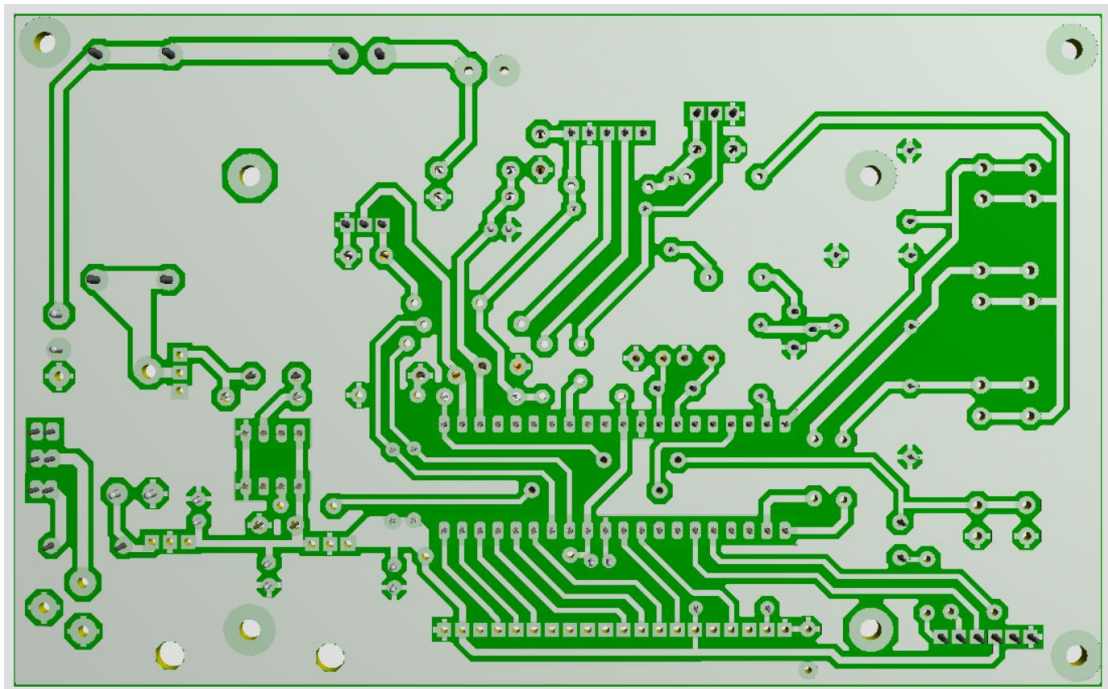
Vue arrière du circuit imprimé de la carte à réaliser en 3D
